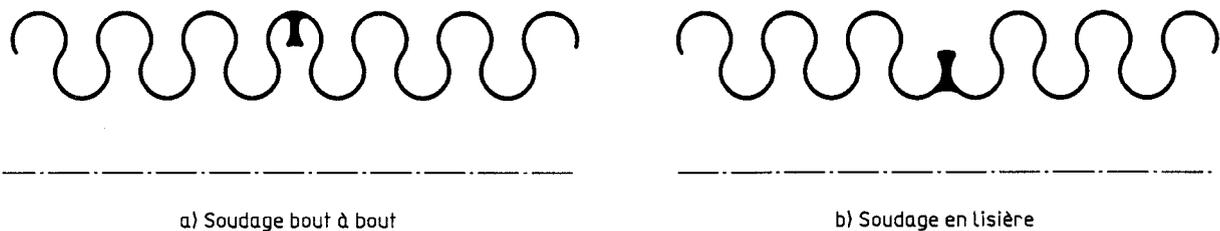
Détails des joints soudés bout à bout et soudés en lisière
